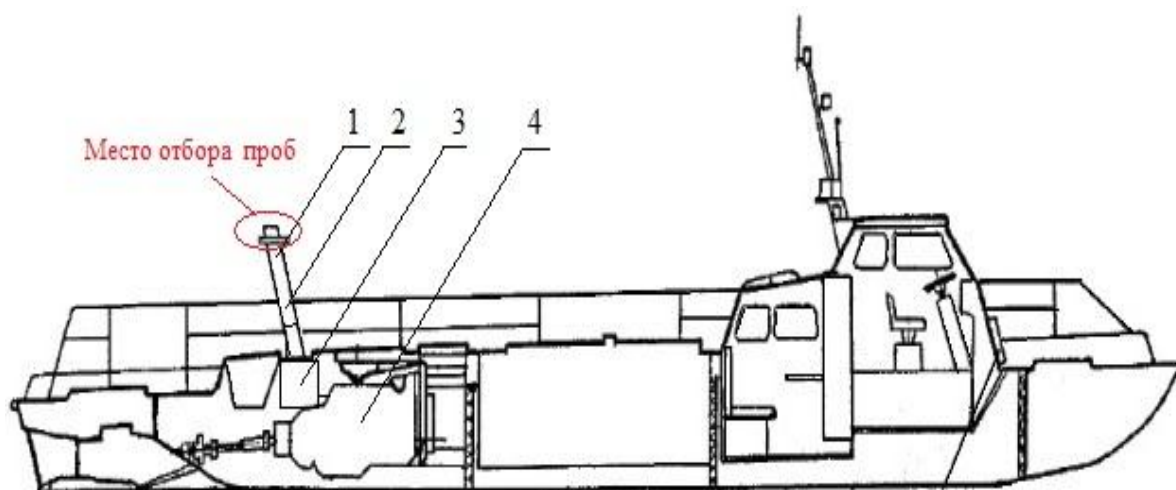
Схема разрезного катера КС-102: 1 – кожух выхлопного трубопровода; 2 – инерционные глушители; 3 – объемные глушители; 4 – двигатель ЯМЗ-238 ГМ2
